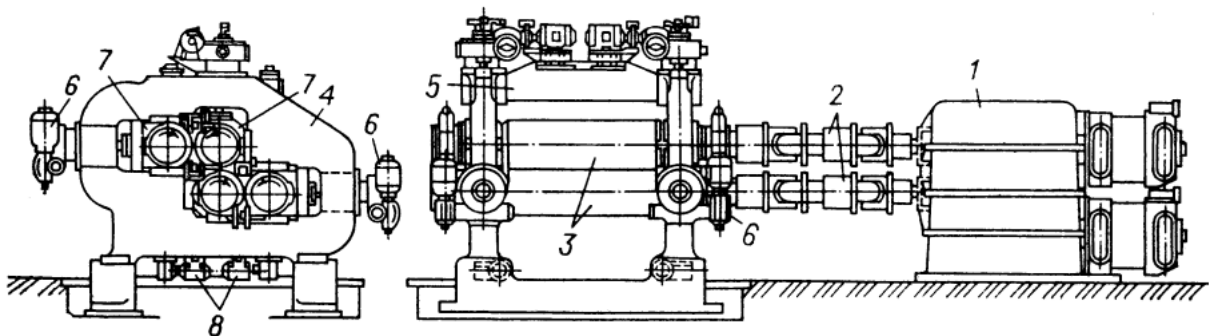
Схеми чотиривалкового Z-подібного каландра: 1 – блок-редуктор; 2 – універсальний шпindel; 3 – валок; 4 – станина; 5 – поперечна траверса; 6 – механізм регулювання міжвалкового проміжку; 7 – валкові підшипники; 8 – механізм перекошування валків
